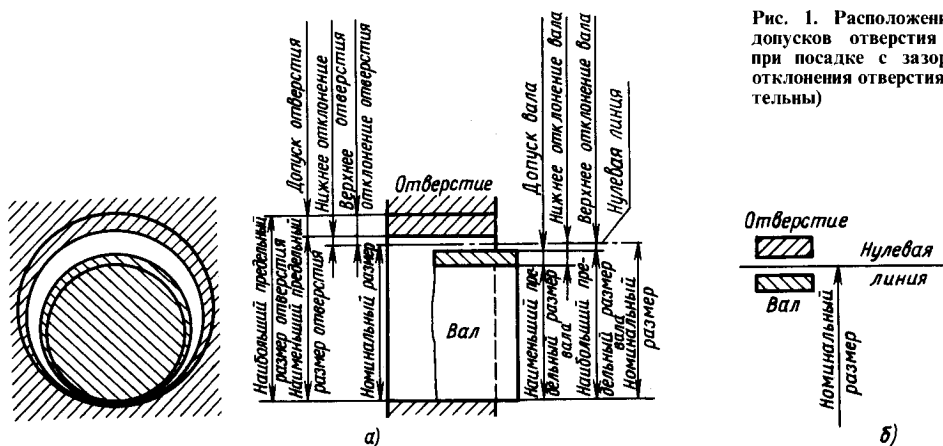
Расположение полей допусков отверстия и вала при посадке с зазором (оба отклонения отверстия положительны)
